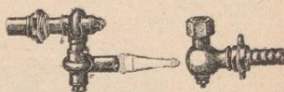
Rundbewegung mit einem Eisenrohrgewinde und Schlauch-Holländer.
